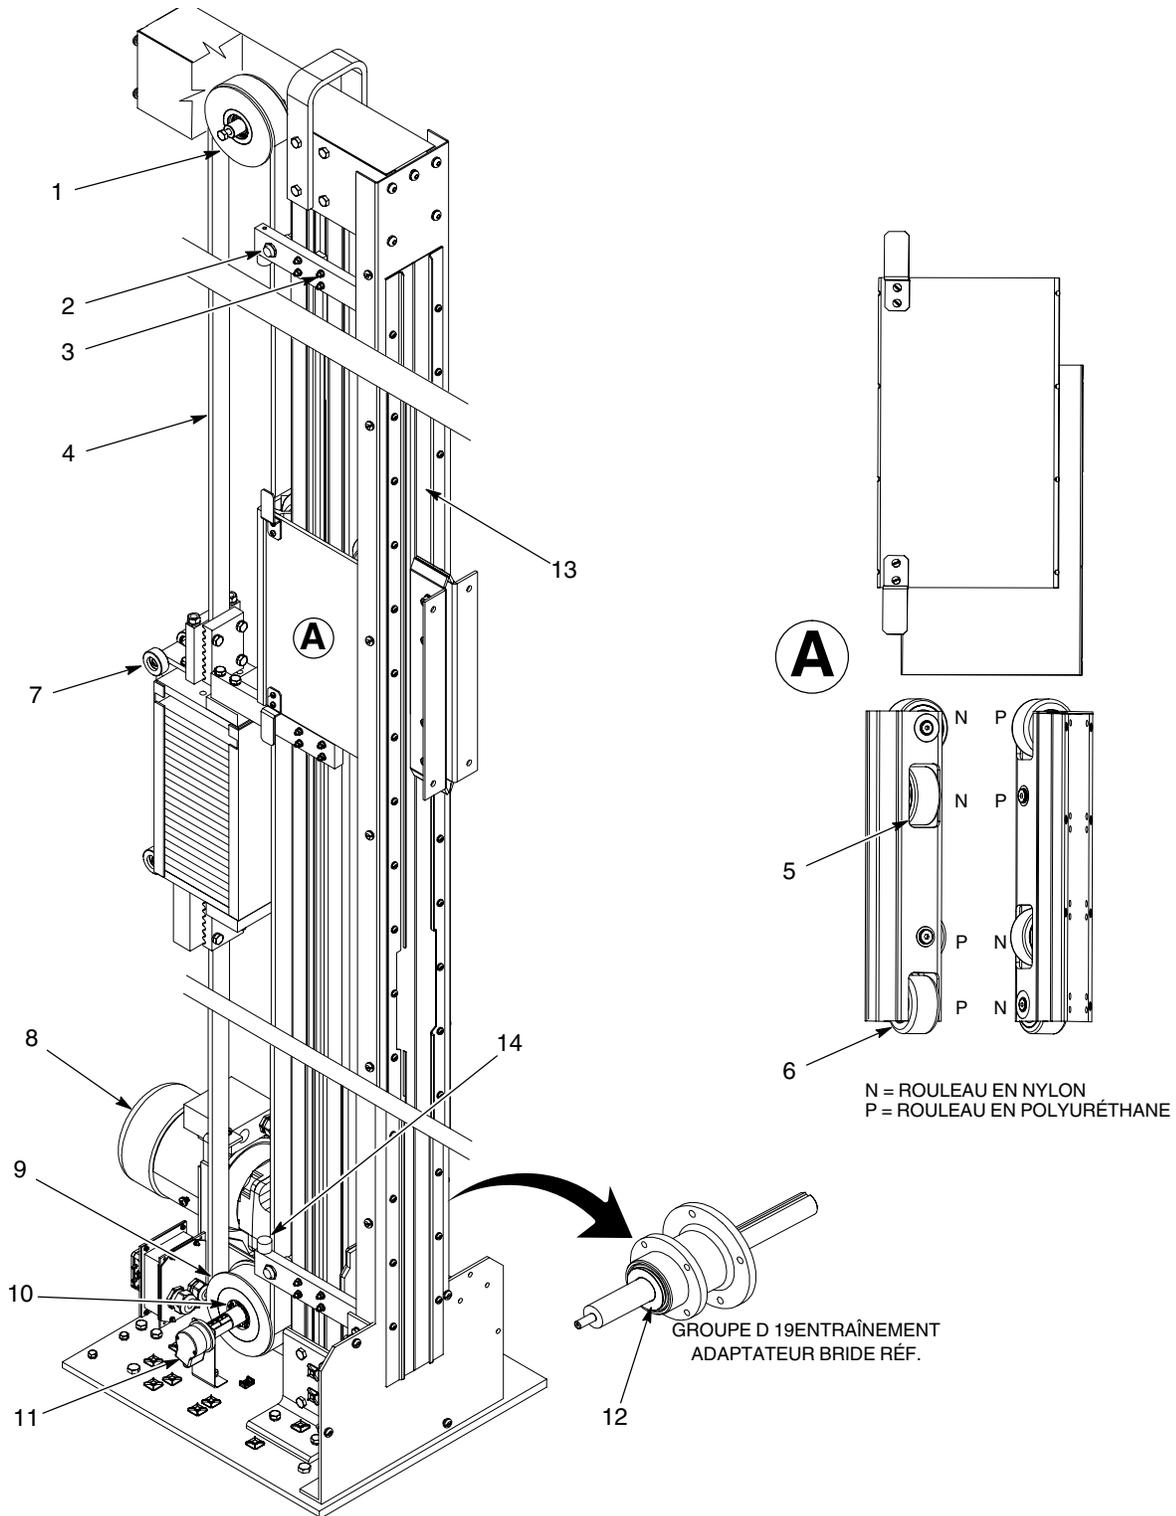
Pièces de rechange du mécanisme de va-et-vient
